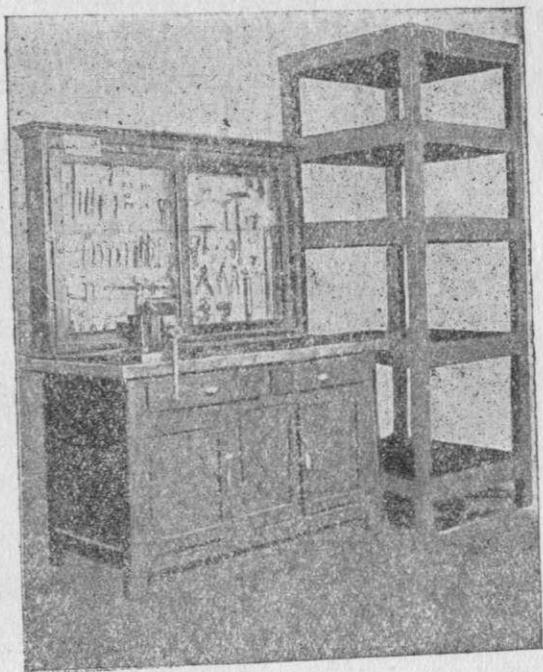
Стандартный верстак с витриной для инструмента и стеллаж для деталей.
